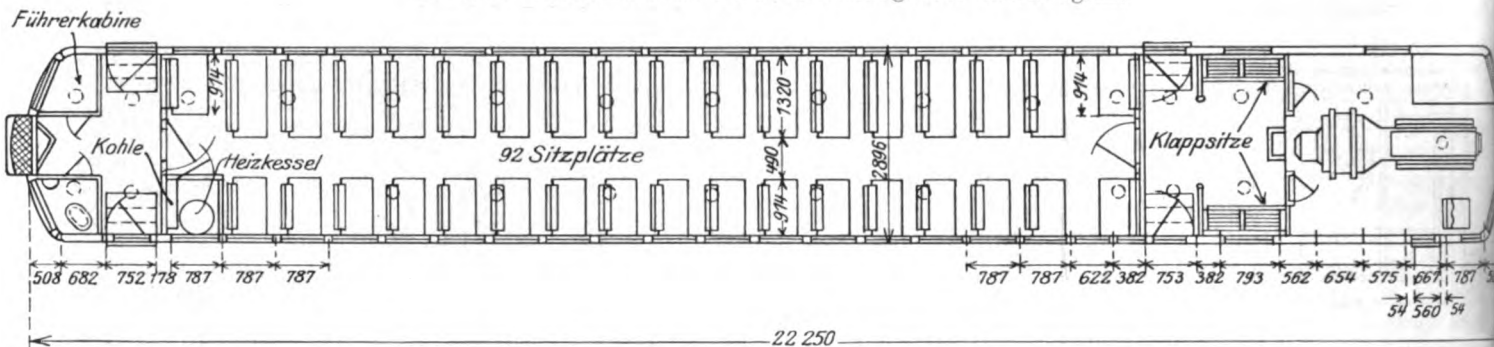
Grundriß des 250 PS Triebwagens Brill. 73 Fuß-Wagen.
